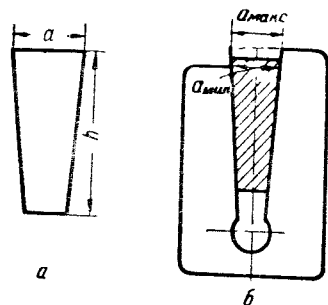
Коллекторная медь: а — профиль коллекторной меди (значения размеров a и h из табл. 124); б — калибр для проверки обработанных коллекторных пластин.
